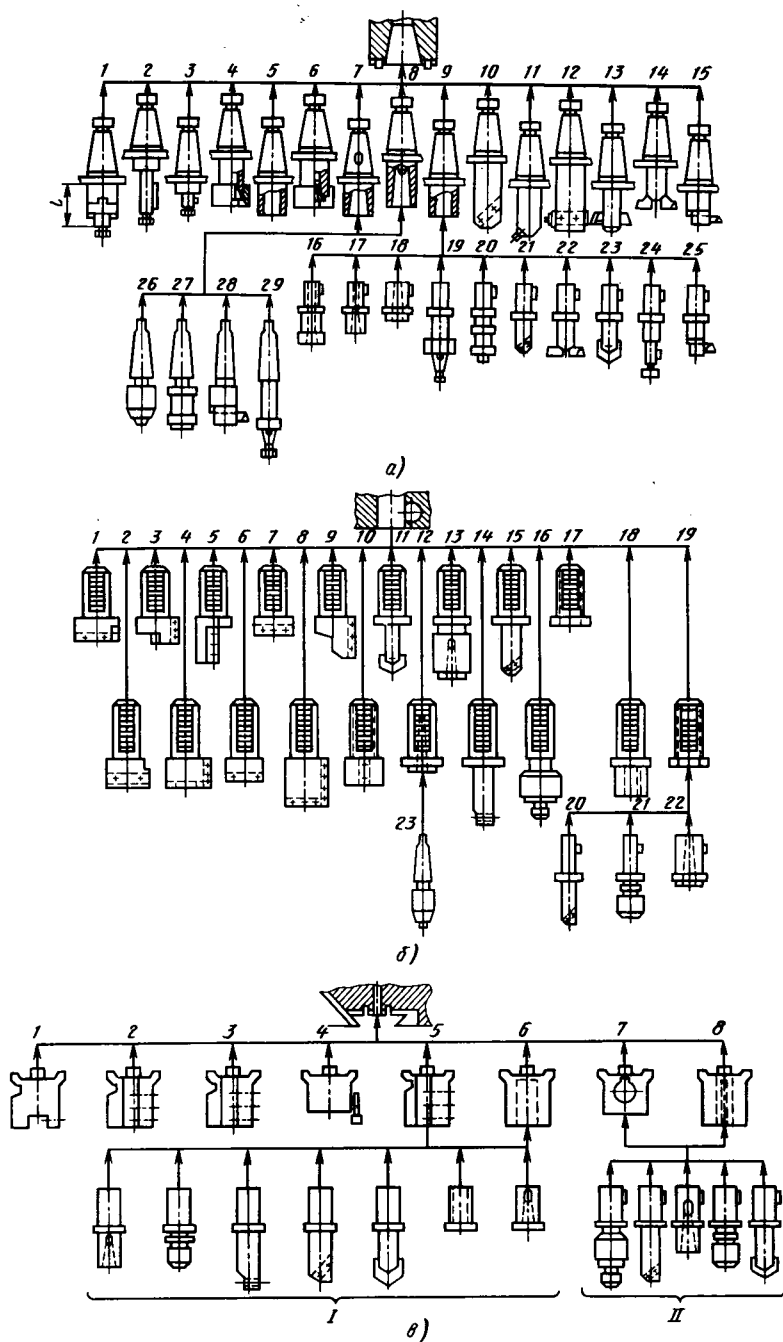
Вспомогательный инструмент для станка с ЧПУ сверлильно-расточной и фрезерной групп:
